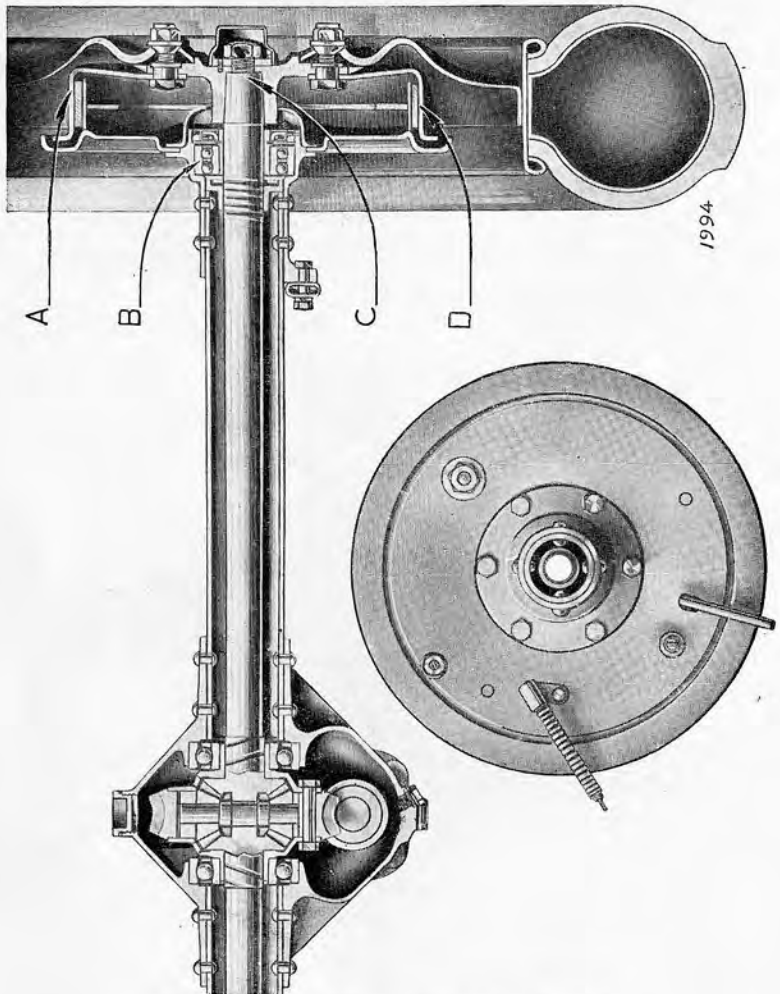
Coupe du pont arrière et vue d'un frein.
